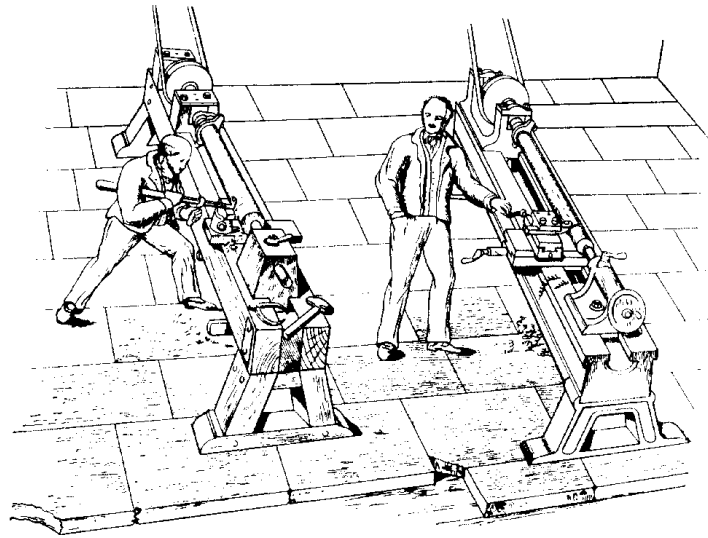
Обробка на токарному верстаті звичайного виконання і на токарному верстаті з механічним супортом Модслі
